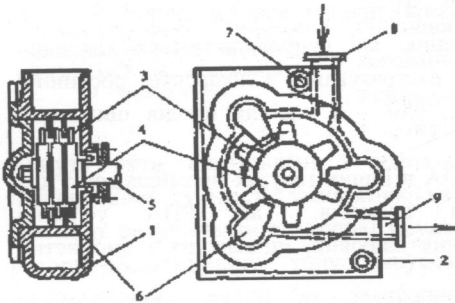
Схема роторно-бильного колоїдного млина:
